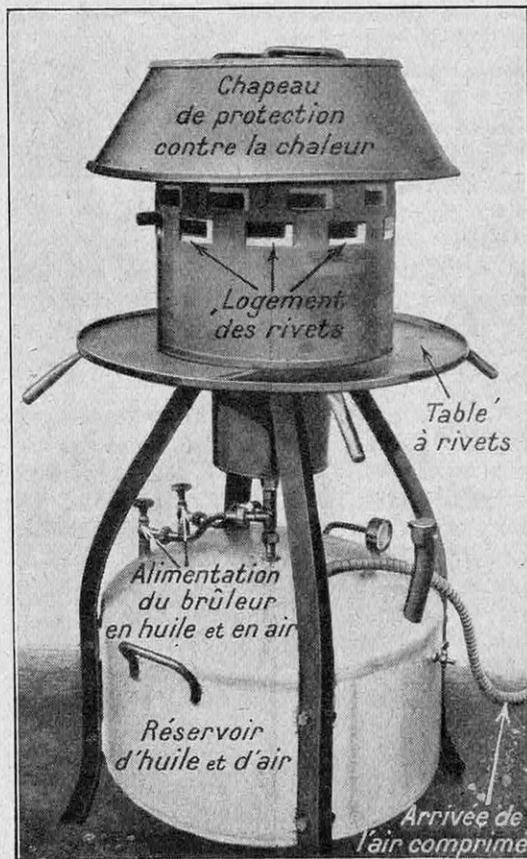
FOUR A CHAUFFER LES RIVETS
